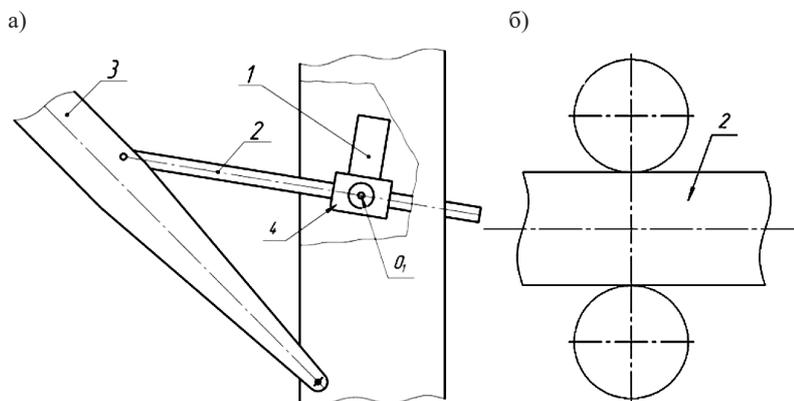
Механизм изменения вылета стрелы перегрузочного крана «Новороссиец»: а — компоновочная схема; б — вид сверху на зацепление рейки 2 с шестернями приводных валов распределителя
